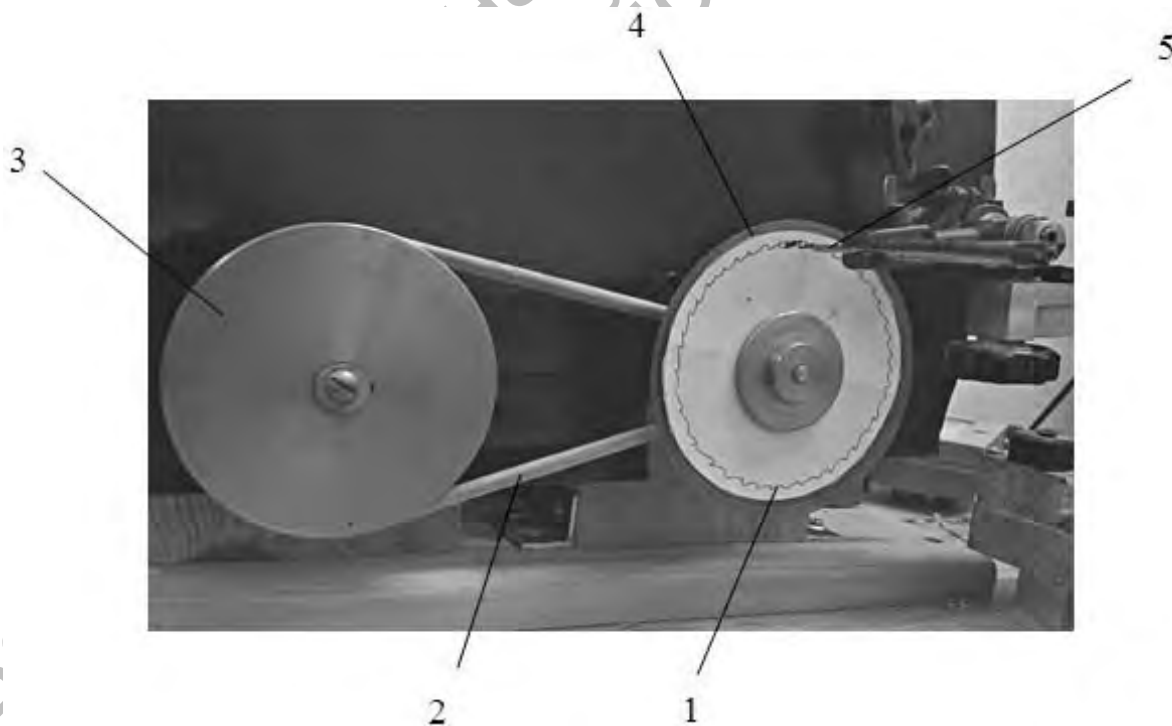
Фотография узла регистрации траектории движения точки, принадлежащей заготовке, на поверхности вращающегося диска
